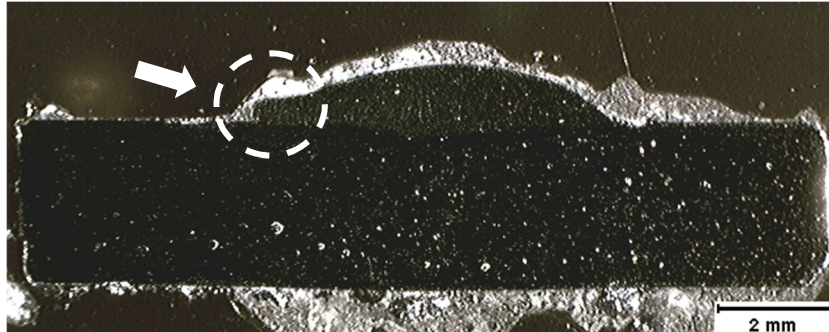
Macrografia (10x) de cordão de solda. Seção transversal O-O do cordão de solda nº 25 – Figura 5.8. Fonte: Autor.
